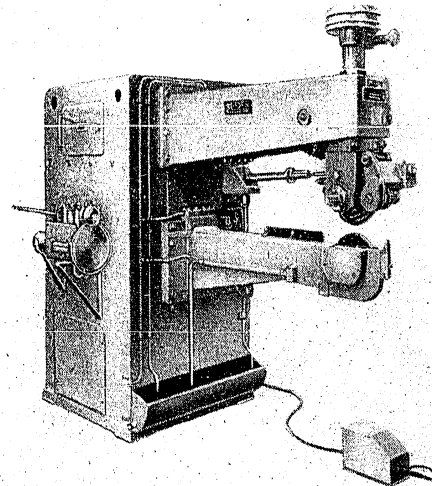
Elektrische Längsnahtschweißmaschine mit zwei Rollenelektroden (Ansicht)
